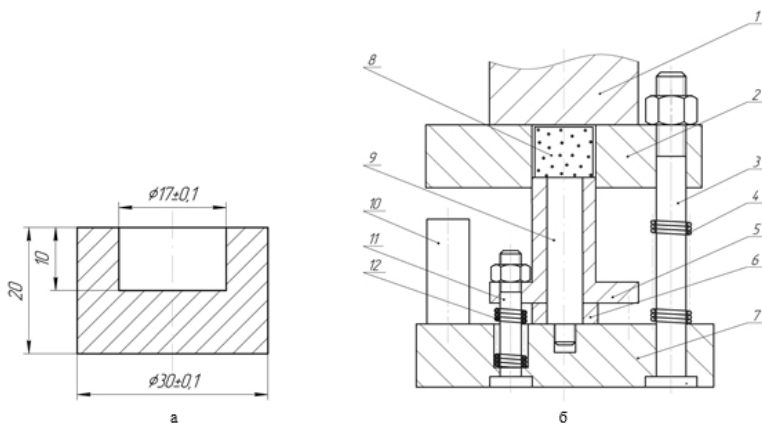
Чертеж детали «заглушка» – а и схема штампа – б
